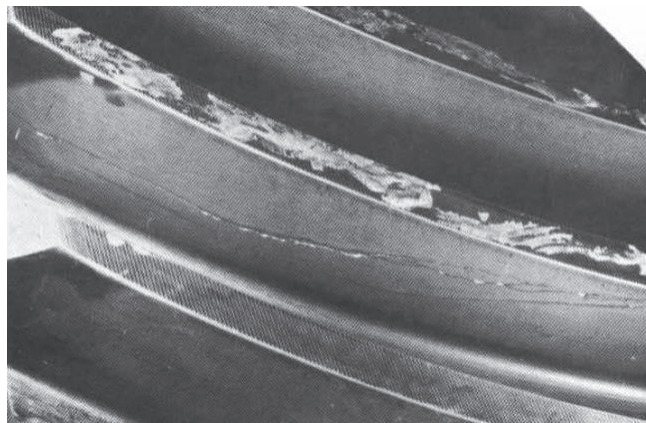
Grietas longitudinales en el flanco.
